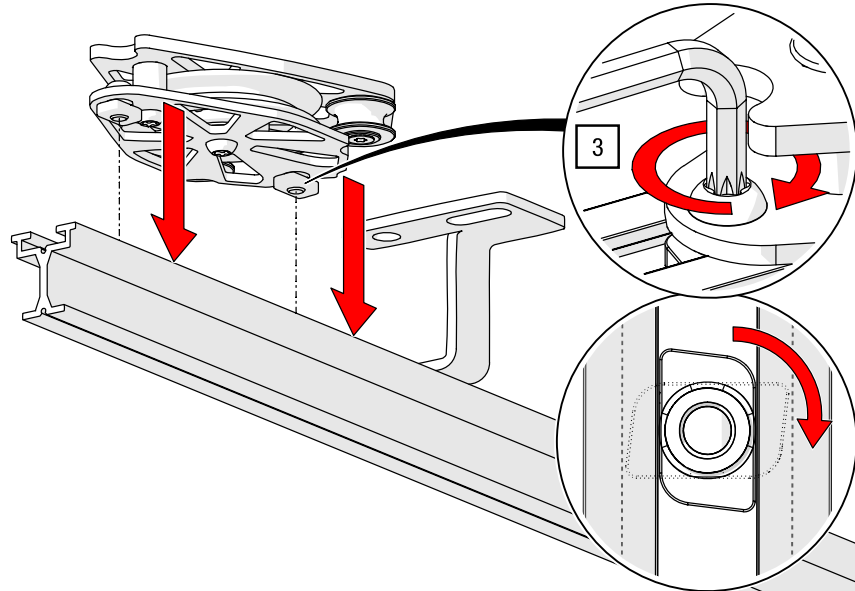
Obenliegende Seilführung – Umlenkrolle montieren
